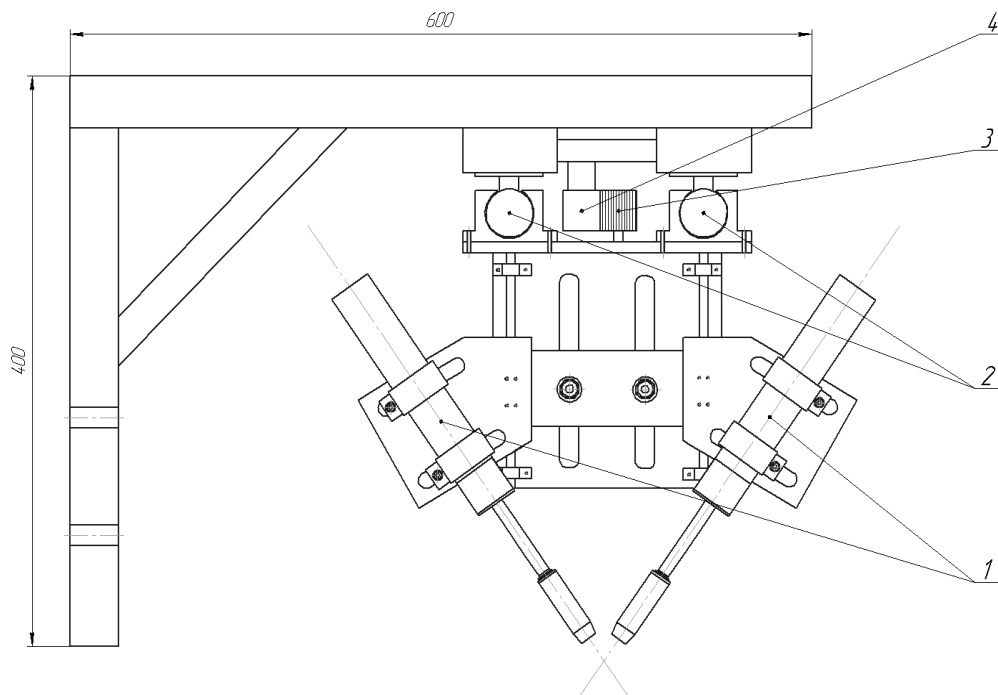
Схема установки для автоматической наплавки комбинацией дуг
